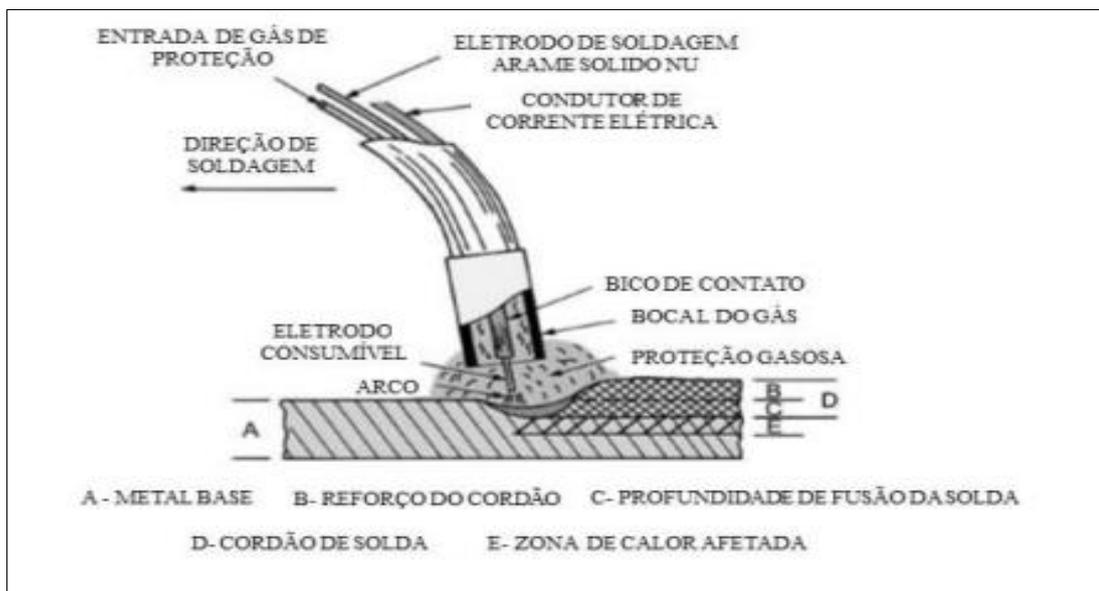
Processo esquemático de soldagem MIG/MAG.
